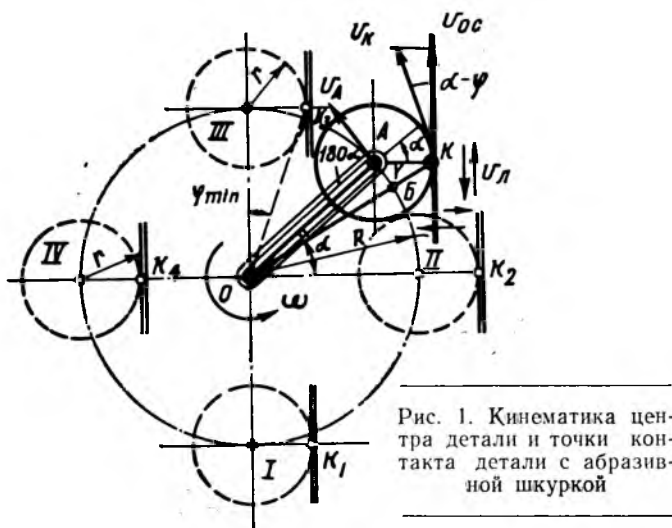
Кинематика центра детали и точки контакта детали с абразивной шкуркой
